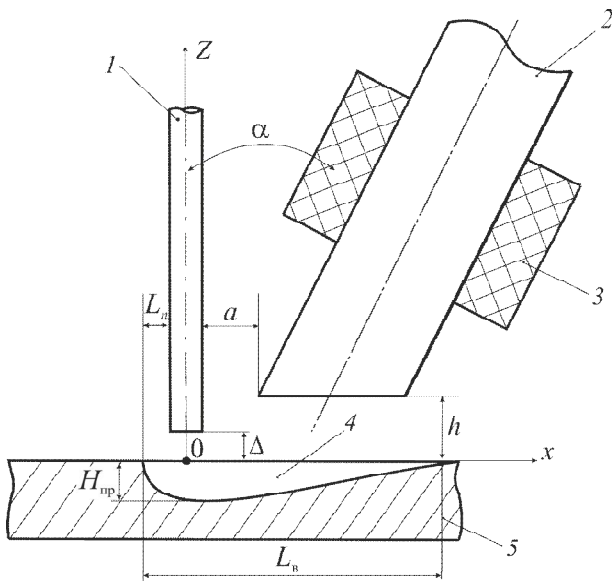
Схема размещения УВ ПРМП над сварочной ванной: 1 – электрод; 2 – стержень; 3 – обмотка; 4 – сварочная ванна; 5 – пластина
